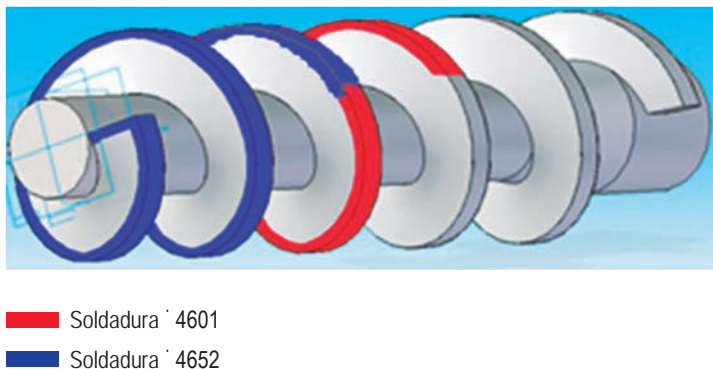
Esquema de recubrimiento para el tornillo con soldaduras.
